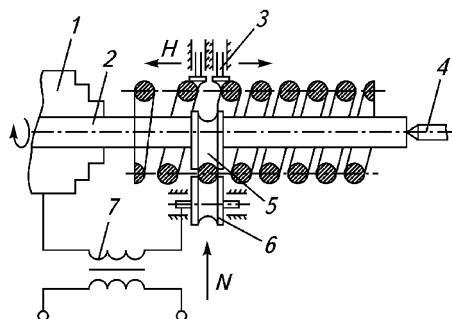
Схема установки для восстановления пружин накаткой:
